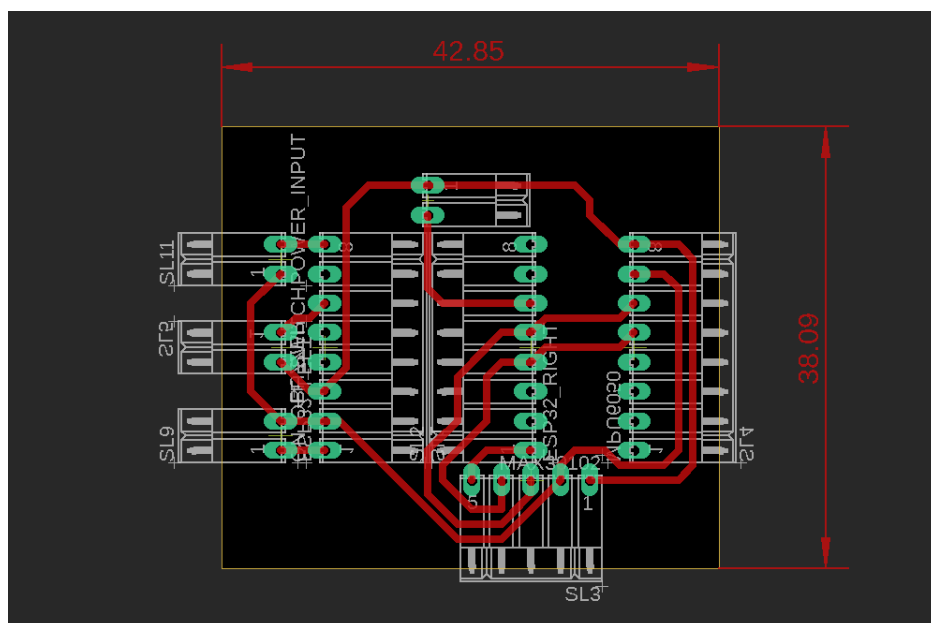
Dimensions principales de la nouvelle configuration du PCB sous EAGLE.
